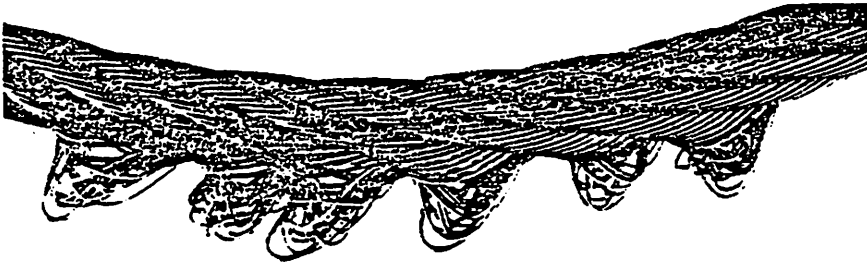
Drahtseil mit Schlaufenbildung von Drähten
